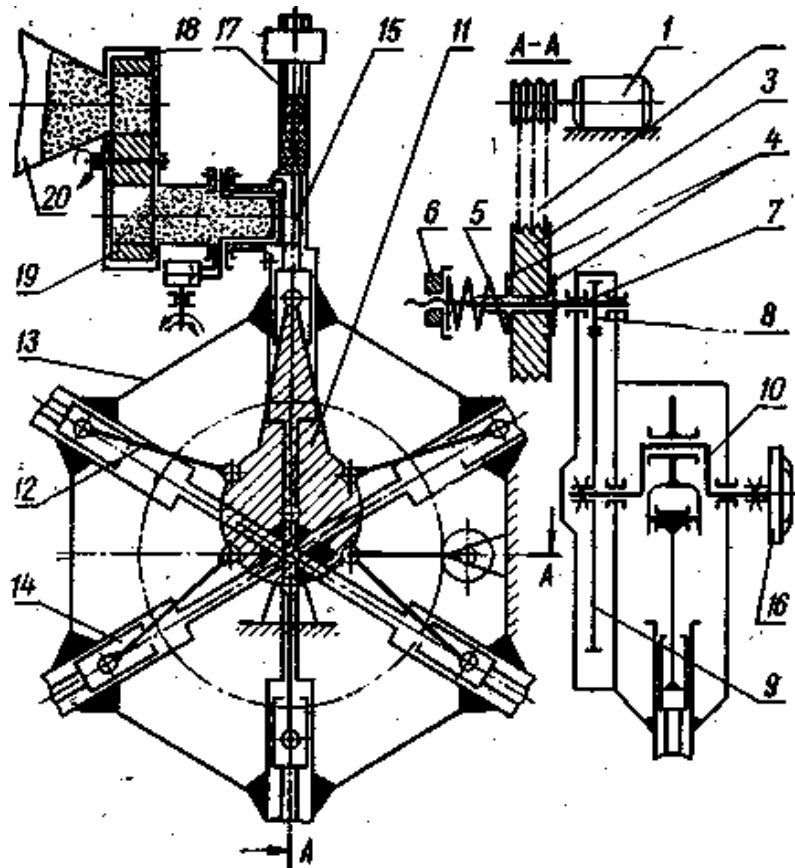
Схема багатоштемпельного преса: 1 – електродвигун; 1 – клинопасова передача; 3 – шків-маховик; 4 – натискні диски; 5 – пружина; 6 – гайка; 7 – вал; 8, 9 – зубчасті колеса; 10 – ексцентрик; 11 – голівка основного шатуна; 12 – причіпний шатун; 13 – направляюча рама; 14 – повзун; 15 – штемпель; 16 – кулачок; 17 – матричний канал; 18, 19 – дисковий живильник; 20 – бункер
